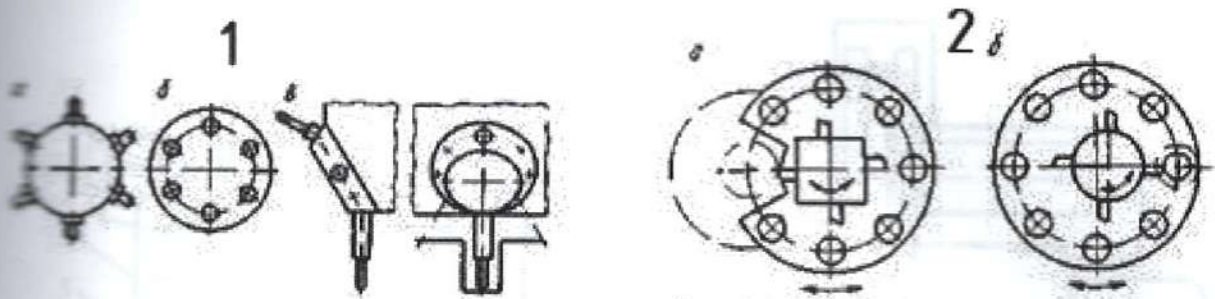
Конструкції револьверних головок токарних верстатів з ЧПК:
